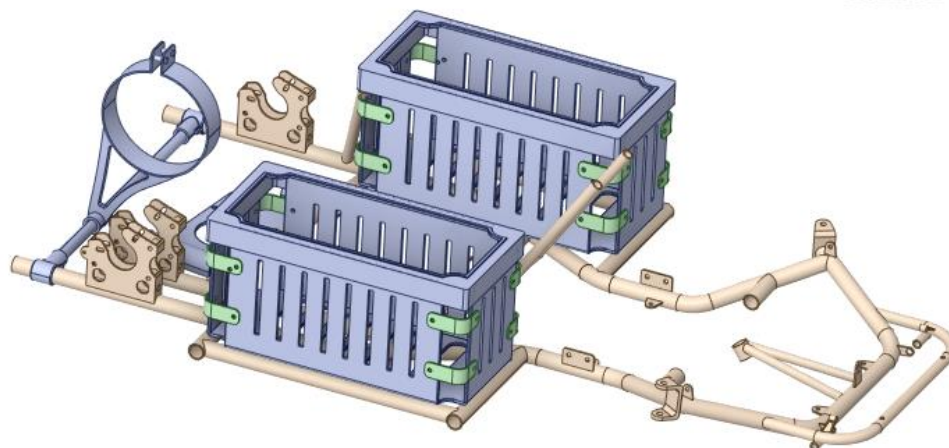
Vista isométrica del ensamble de los soportes sobre el chasis
